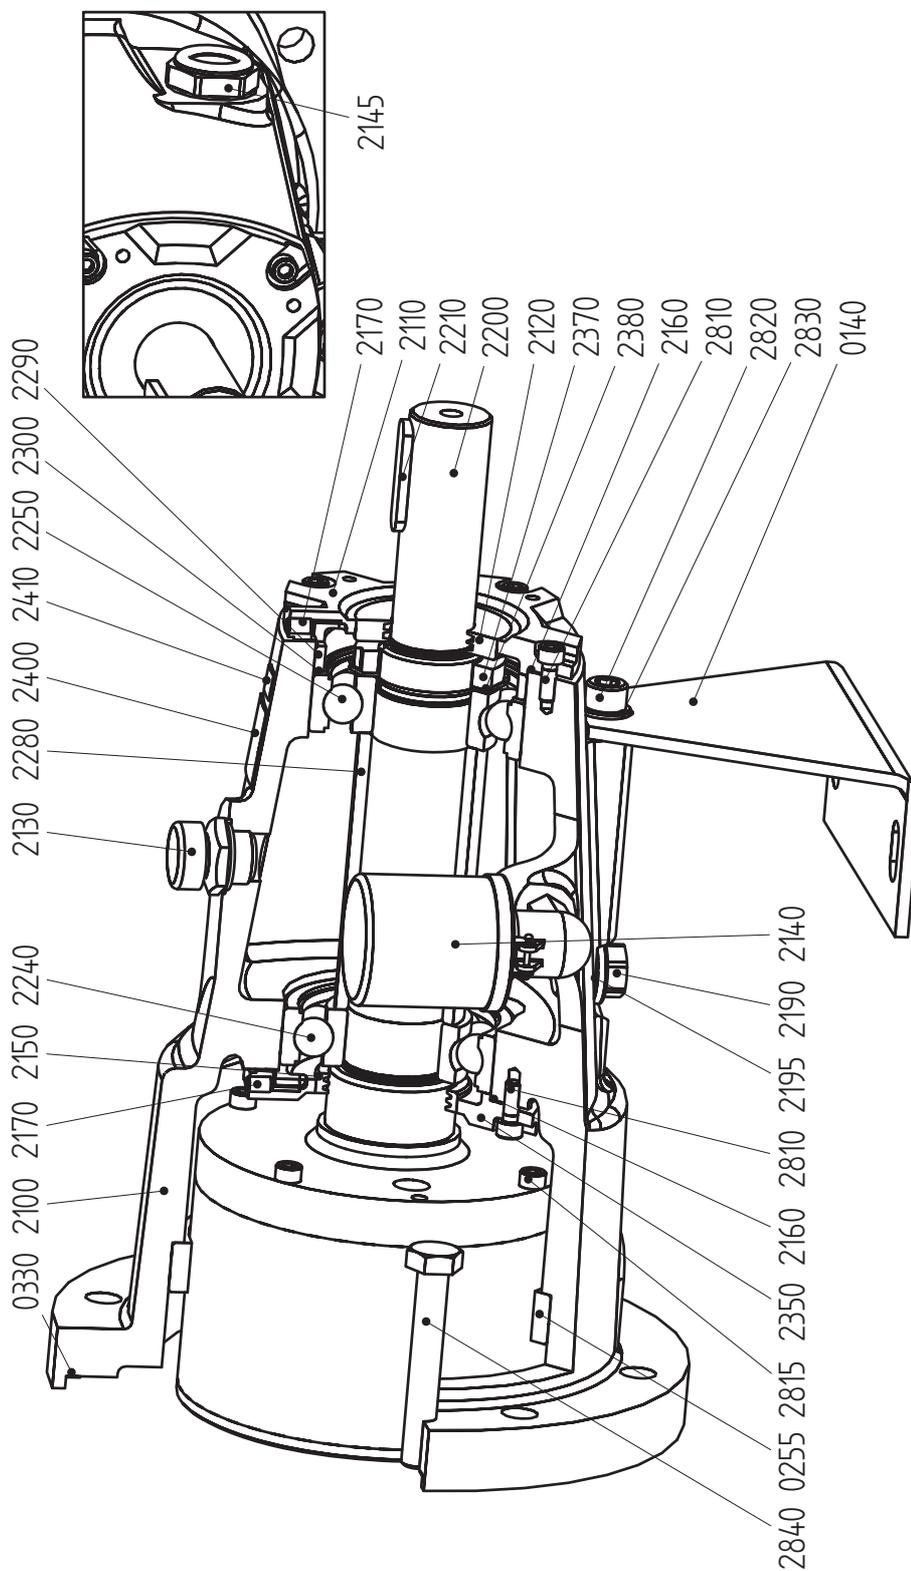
Роликовый подшипник L3 с масляной смазкой
